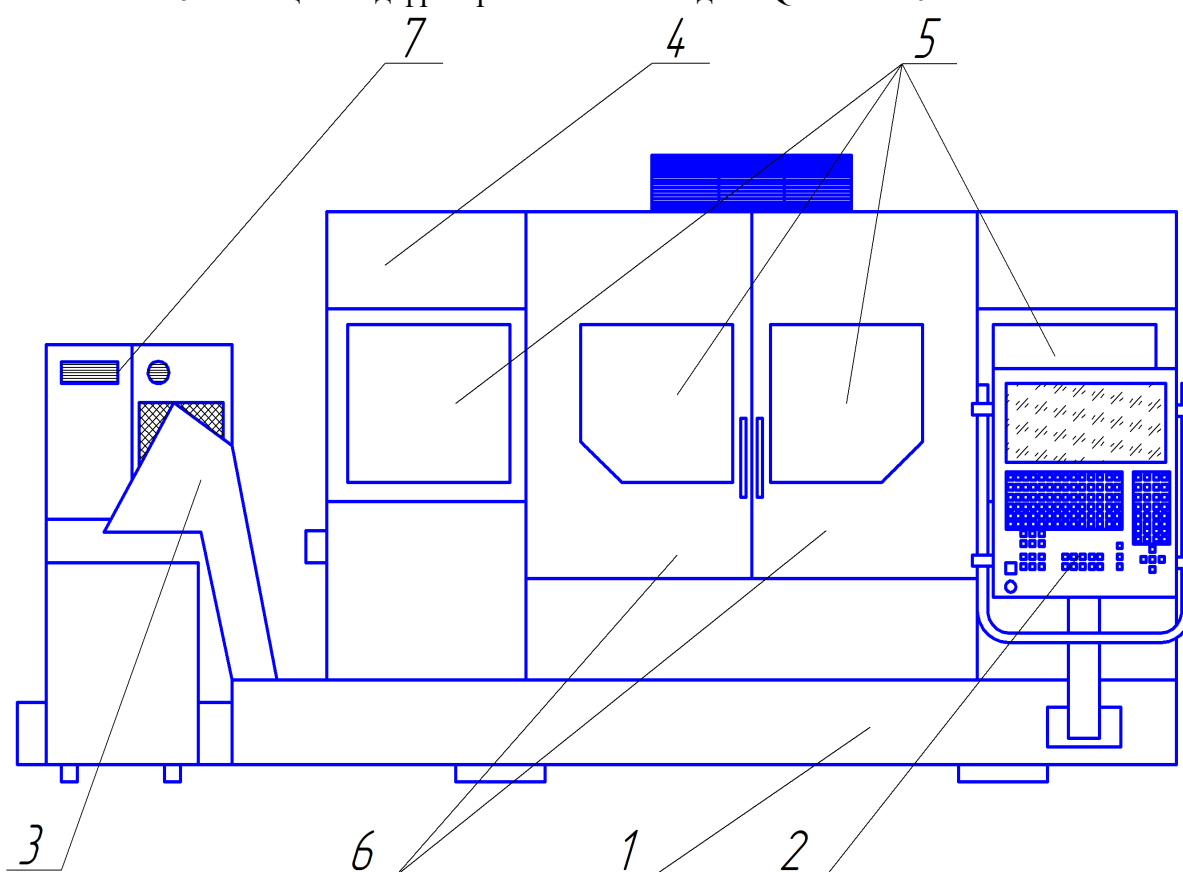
Основные узлы фрезерного станка модели Quaser M204CU с ЧПУ
